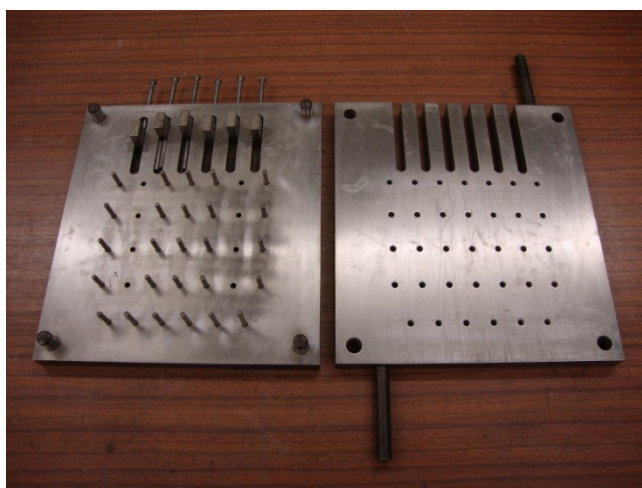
Molde utilizado para fabrico provetes DCB e ENF
